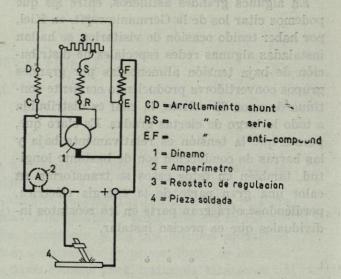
Esquema de una dínamo de soldadura Brown Boveri
